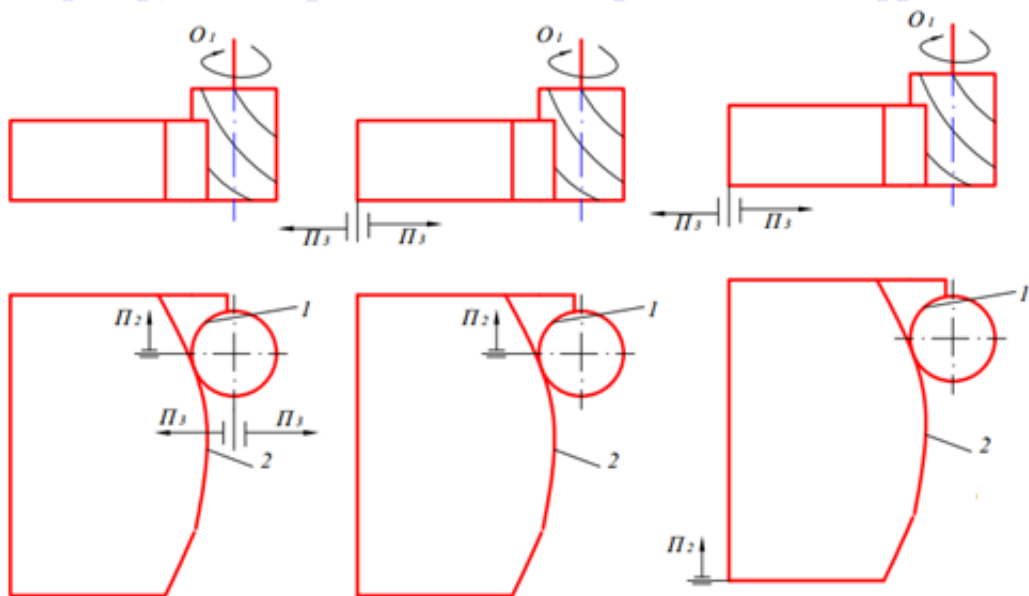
Фрезерування криволінійної поверхні кінцевою фрезою
